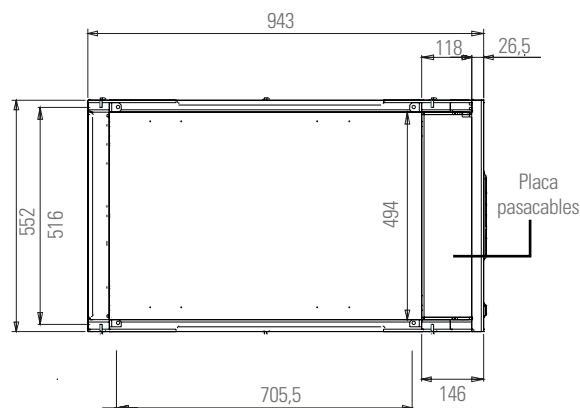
Vista en planta de la base de equipos de 80... 160 kVA.
